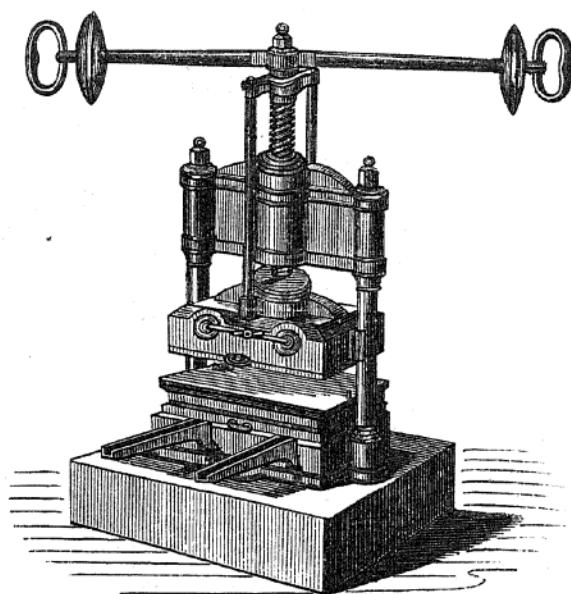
Золотильный прессъ съ маятникомъ и низкой двигающейся доской фабрики
